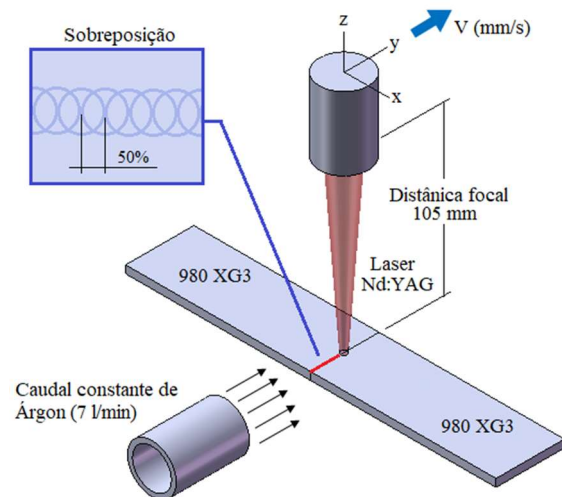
Esquema representativo do processo de soldadura do aço Gen3 980T
